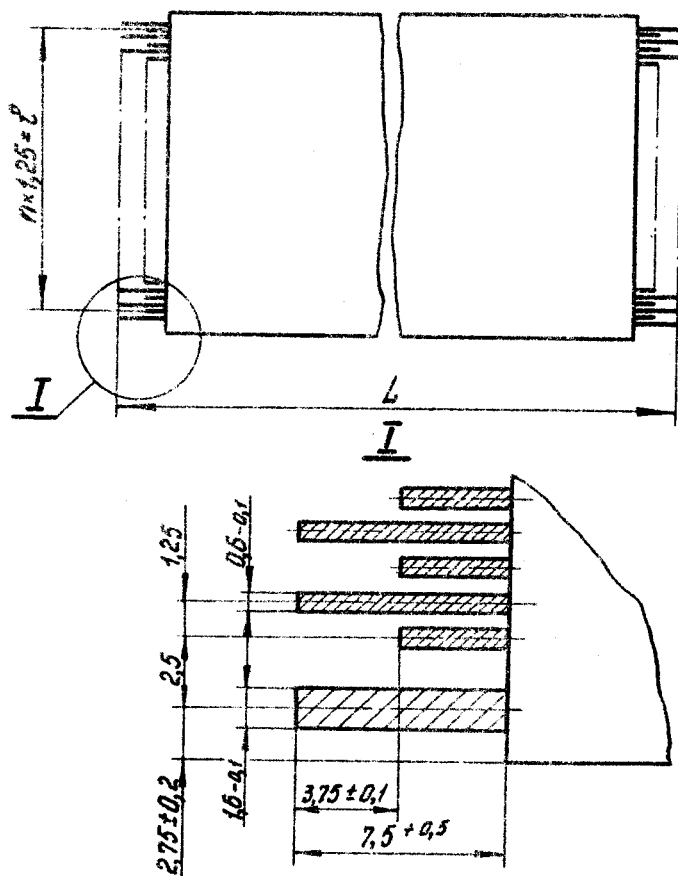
Гибкий печатный кабель с двухрядными контактными лепестками.
